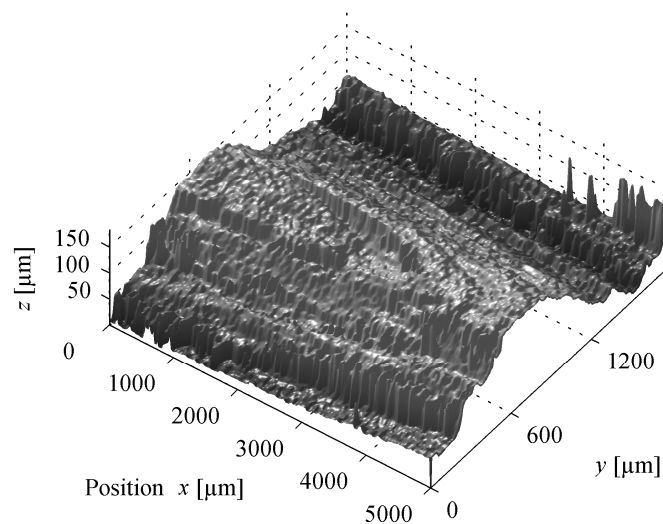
Topographie einer Schweißnaht. Deutlich tritt die so genannte Schweißbraupe hervor, die sich prozessbedingt ausbildet.
